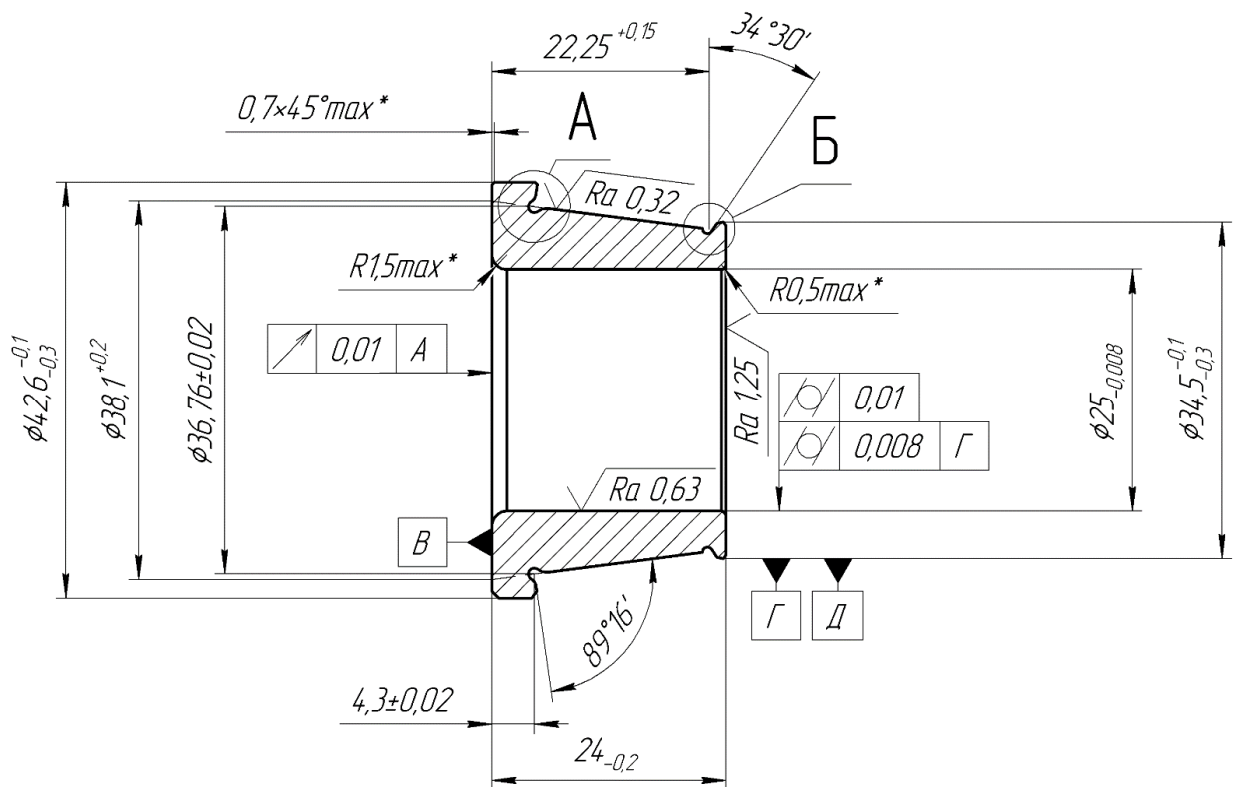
Чертеж внутреннего кольца подшипника 7605А
